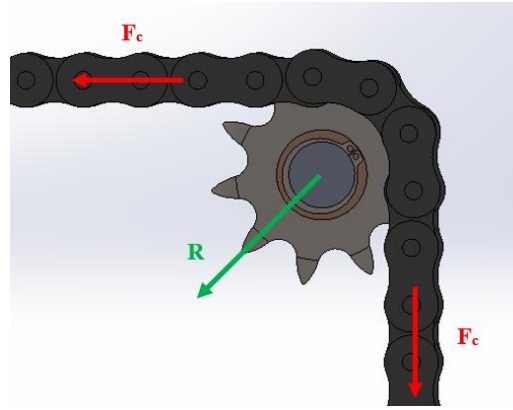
Análisis de fuerzas sobre el eje del engranaje chico.
